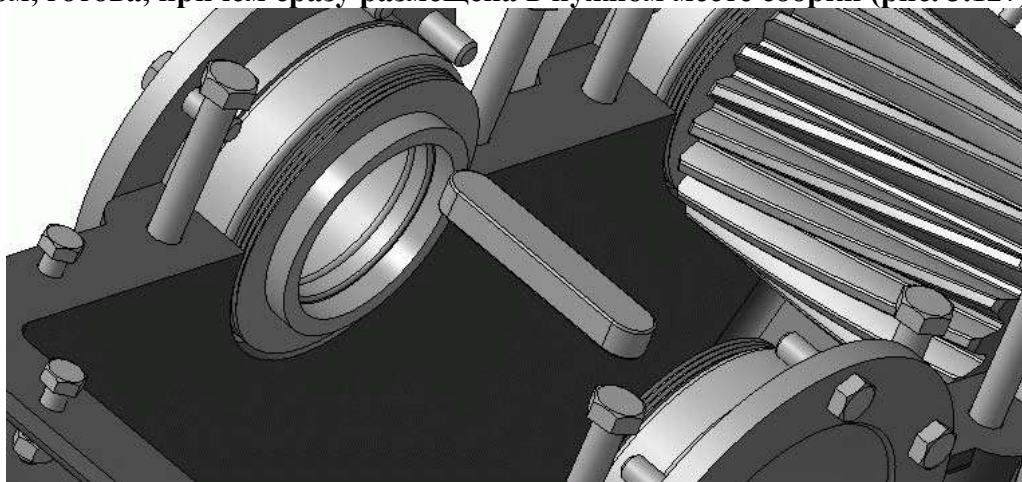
Деталь шпонки, смоделированная прямо в сборке (крышка редуктора, зубчатое колесо и ведомый вал скрыты)
